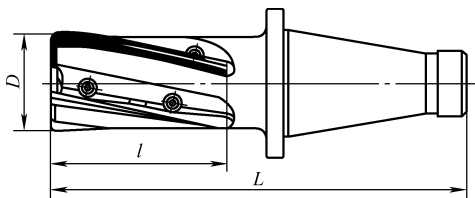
体育馆看台模型加工用的 TURN 旋铣刀具
